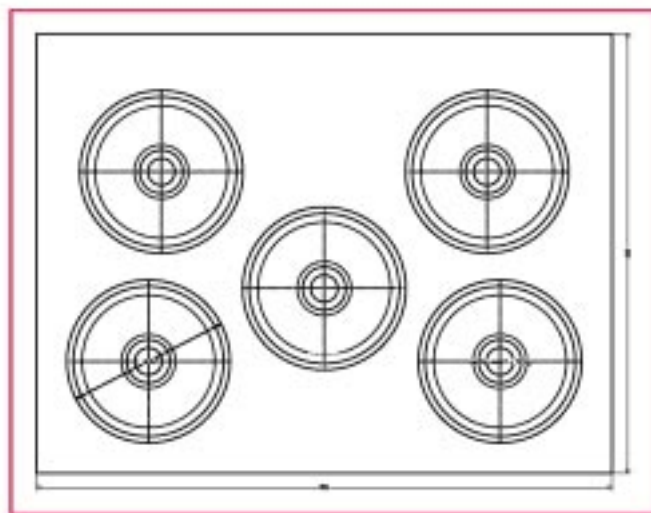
Layout generico della placca metallo per il calcolo e la progettazione dell'impianto di colata.
